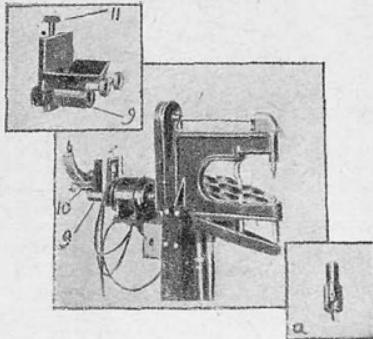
Отдельные части станка для сверления и клепки Феродо
